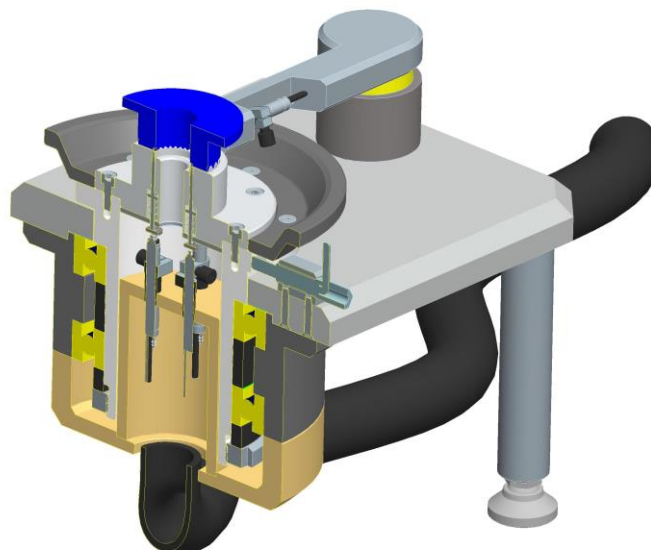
Messvorrichtung für Lückenmessung und Rundlaufmessung
